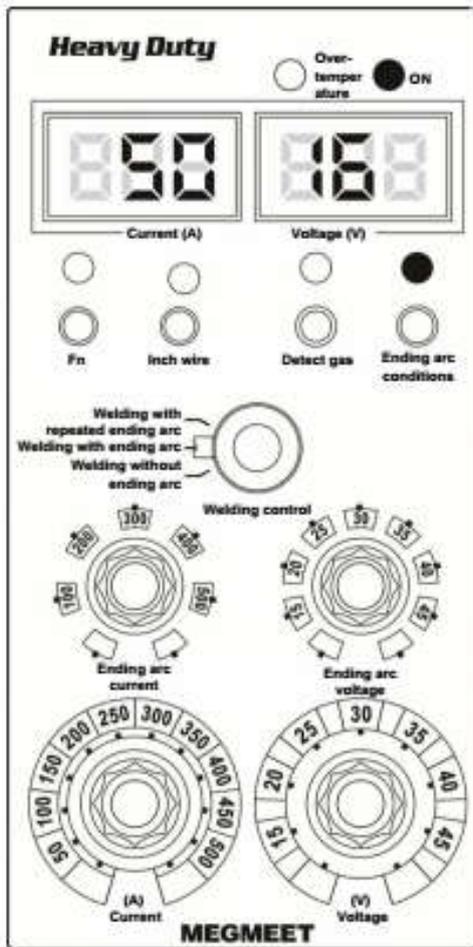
Выбор сварки с режимом повторной заварки кратера
